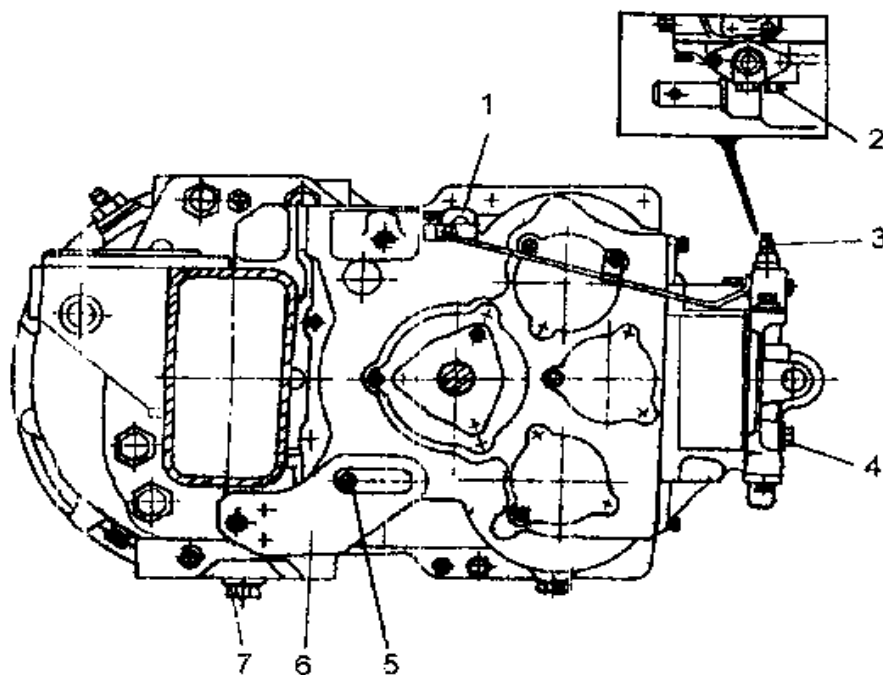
Коробка диапазонов (вид слева): 1 – первичный преобразователь (датчик) указателя скорости движения; 2 – болт крепления механизма переключения диапазонов; 3 – трубка клапана прокачки гидросистемы блокировки; 4 – пробка отверстия для заливки и контроля уровня масла коробки диапазонов; 5 – демонтажный болт; 6 – кронштейн для демонтажа коробки диапазонов; 7 – пробка отверстия слива масла из коробки диапазонов
